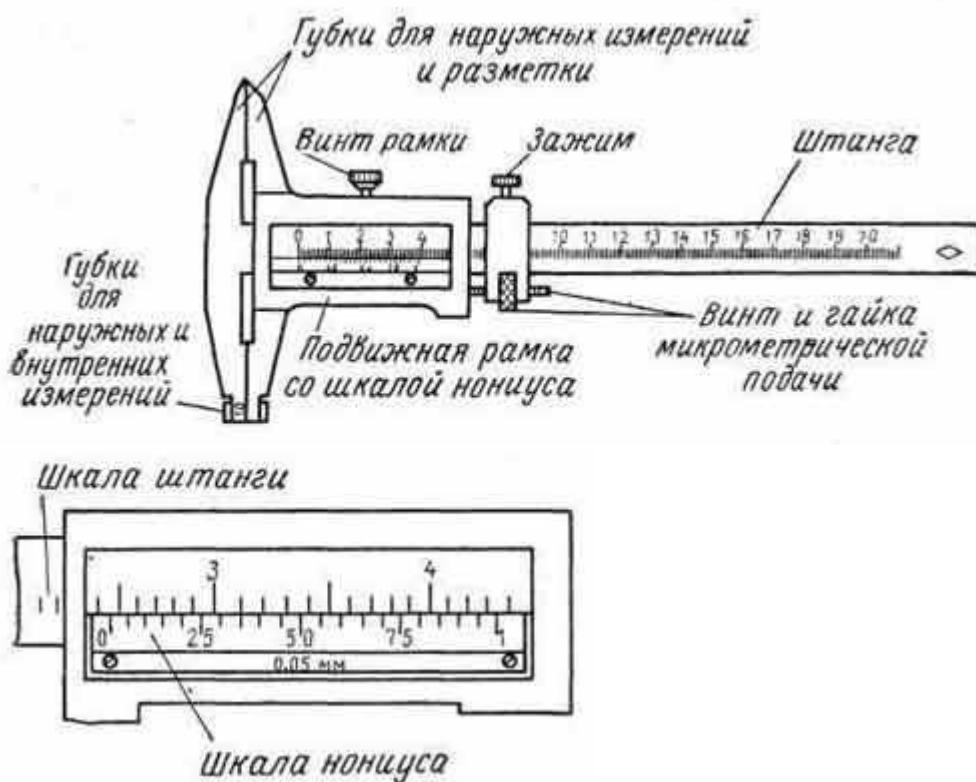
Конструкция штангенциркуля типа ШЦ-II
